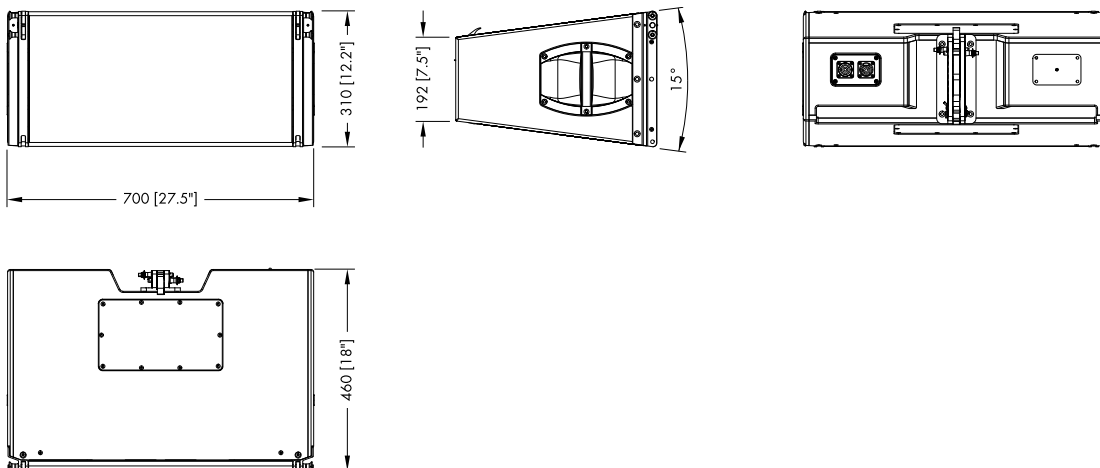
Dimensioni del cabinet V8/V12 in mm [pollici]
